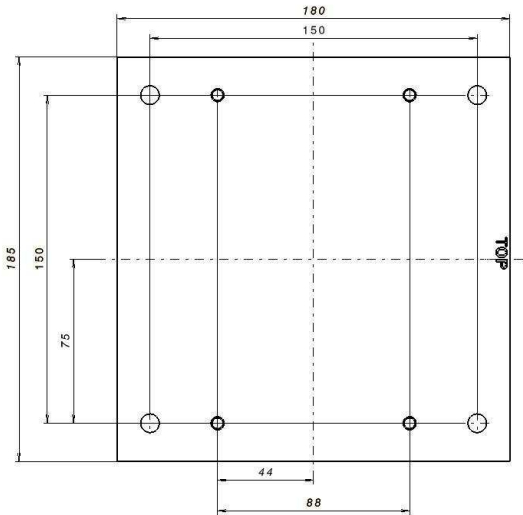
Bohrbild Standard-Wand- Adapterplatte BG D
